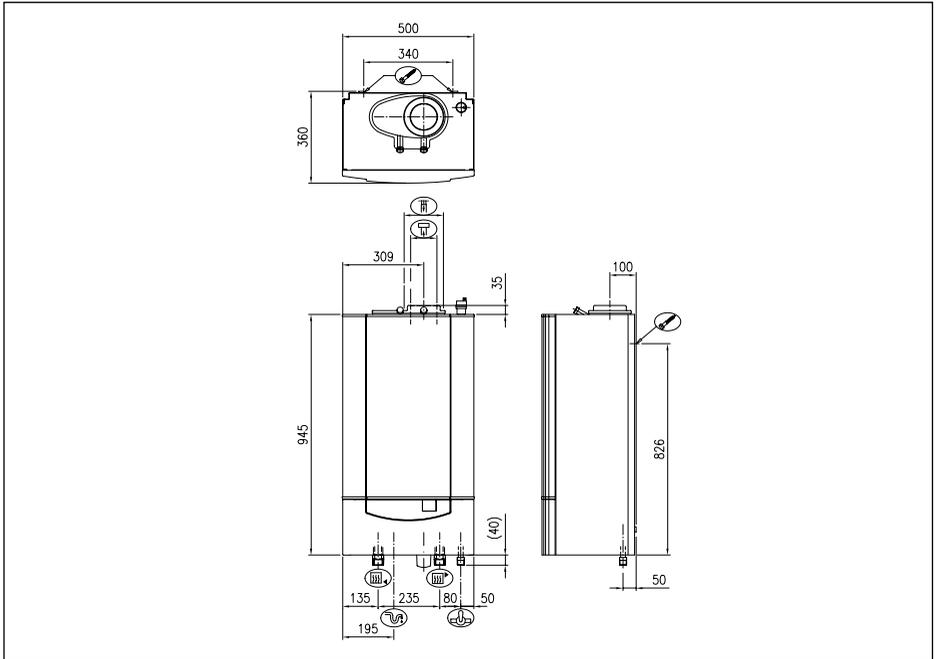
Dimensions Remeha Quinta 45 et Quinta 65
